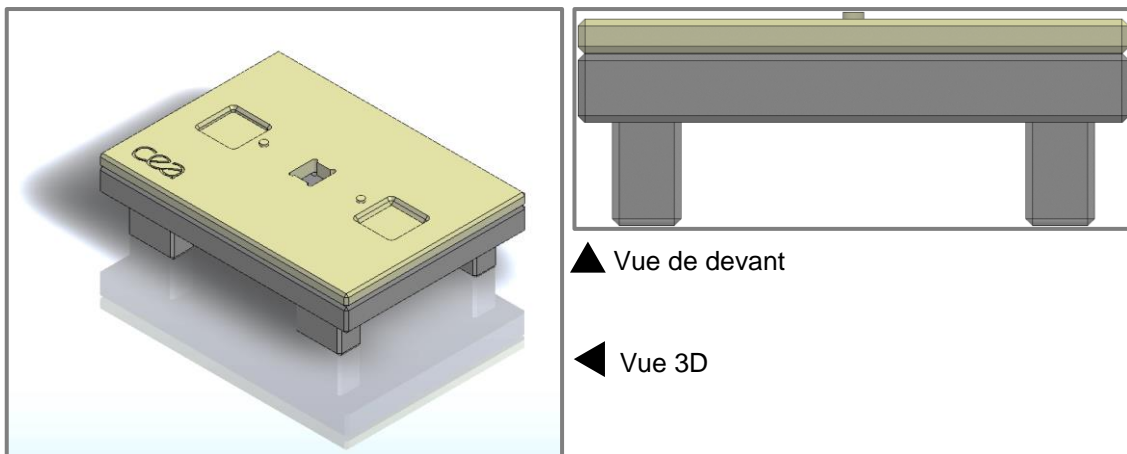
Vues de l'assemblage entre le support en aluminium et la plaque plastique dans laquelle sont usinées plusieurs cavités.
